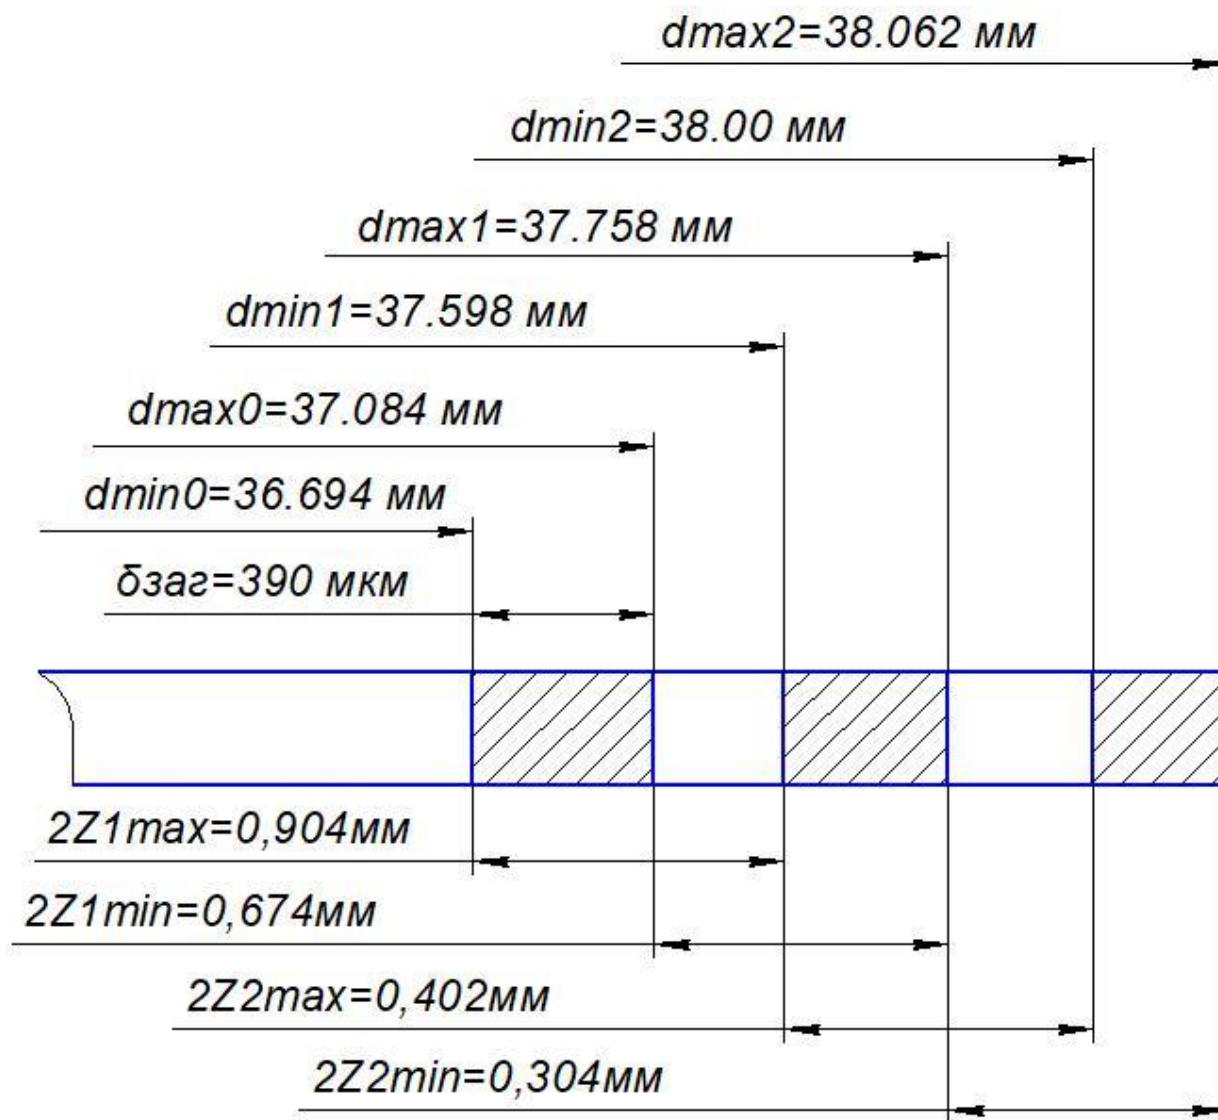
Схема графічного розміщення припусків та допусків на обробку поверхні $\varnothing 38(H9)^{+0.062} ..$
